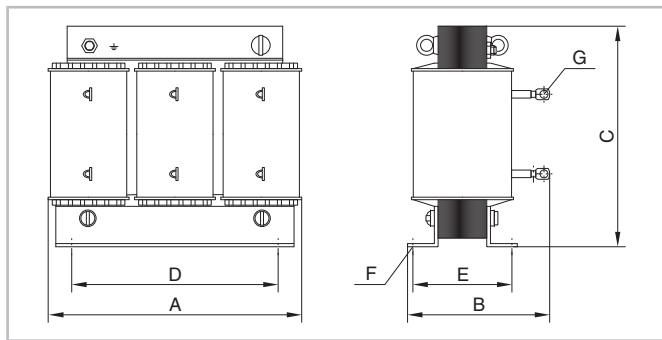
Габаритные чертежи линейных реакторов 182-KS.. 330-KS
